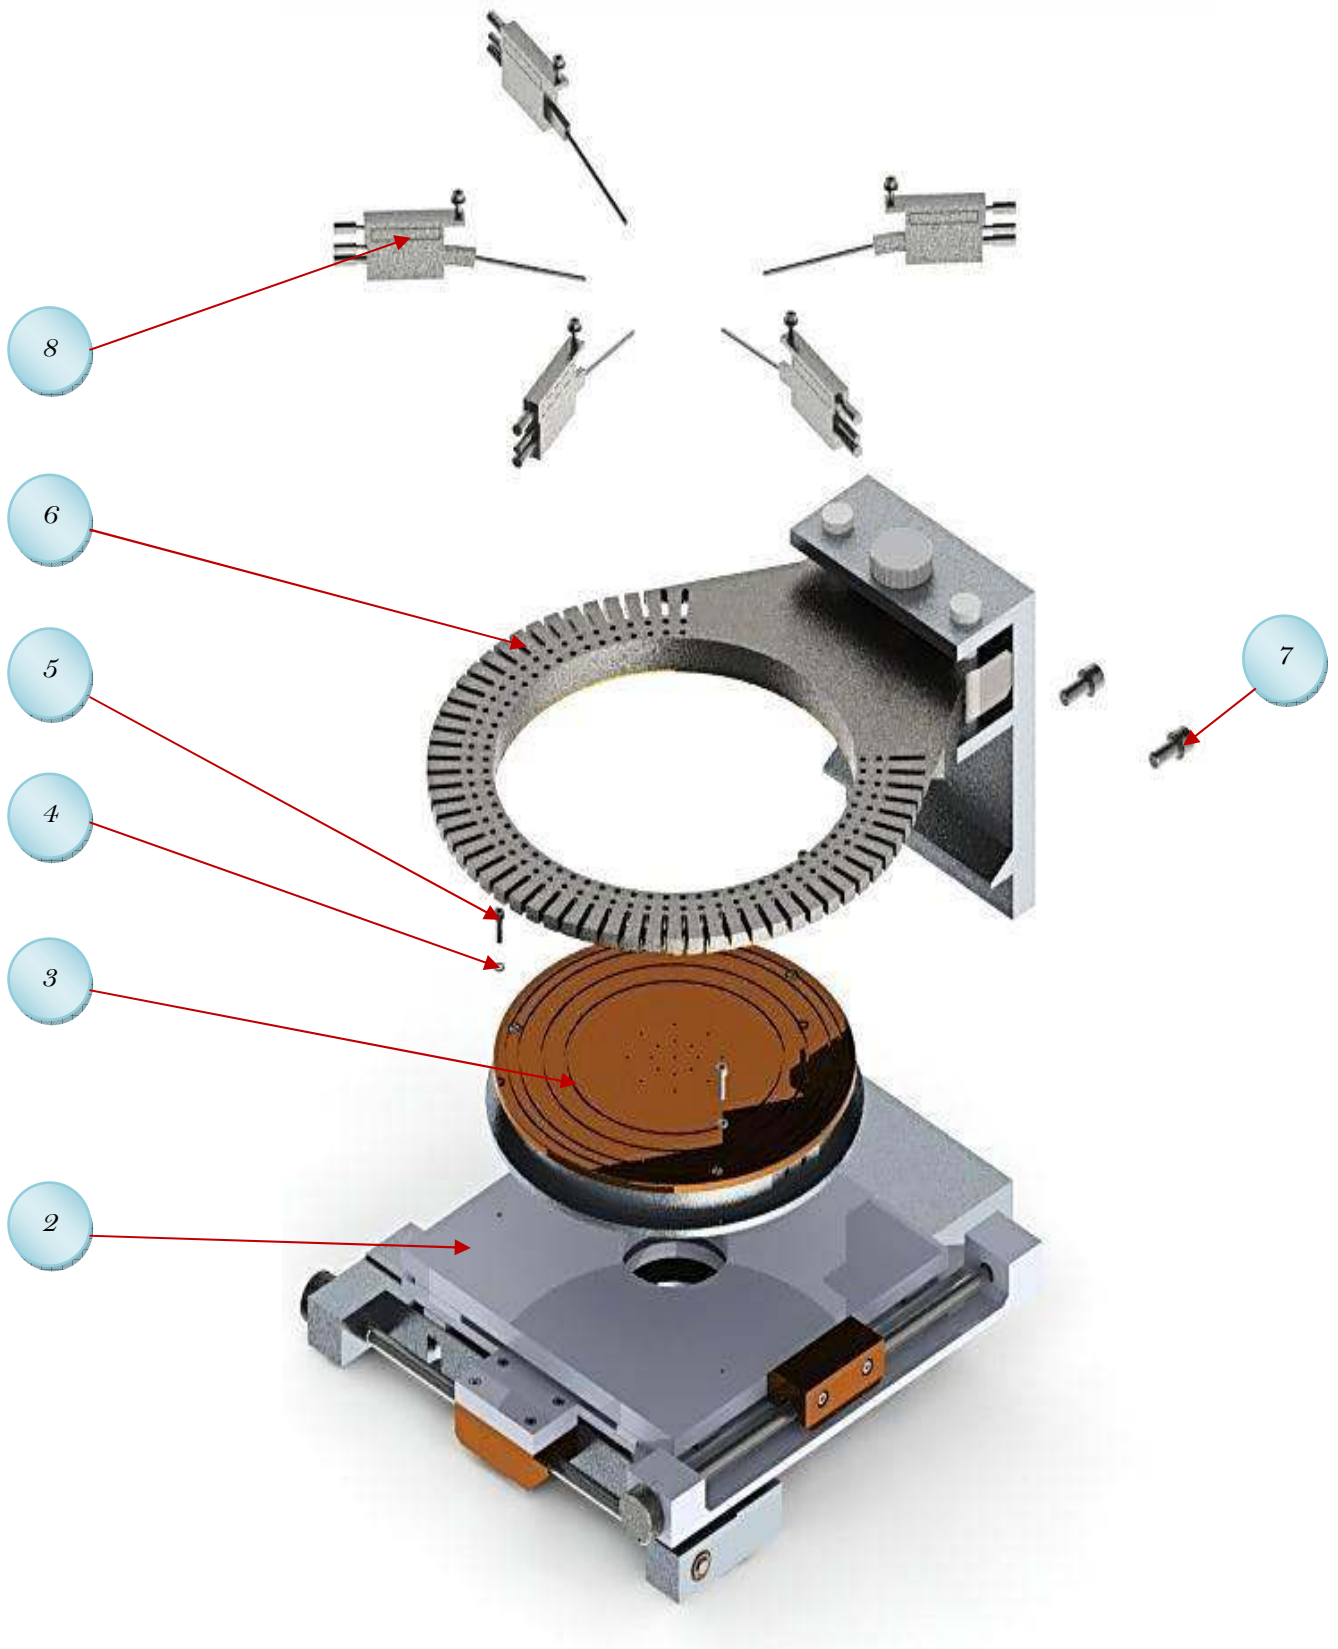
Vue éclatée de tester sous pointes, réalisé par solide Works
